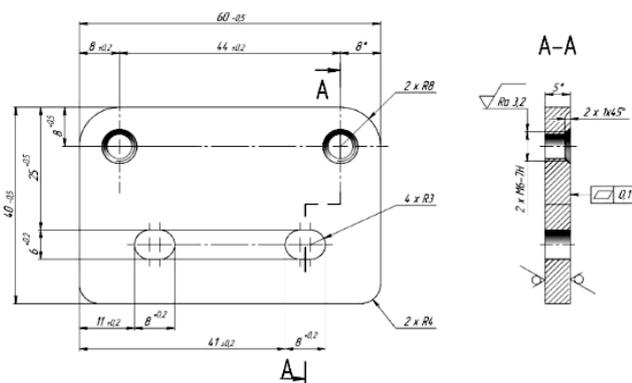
Чертеж детали, созданный в ПО Fusion 360
